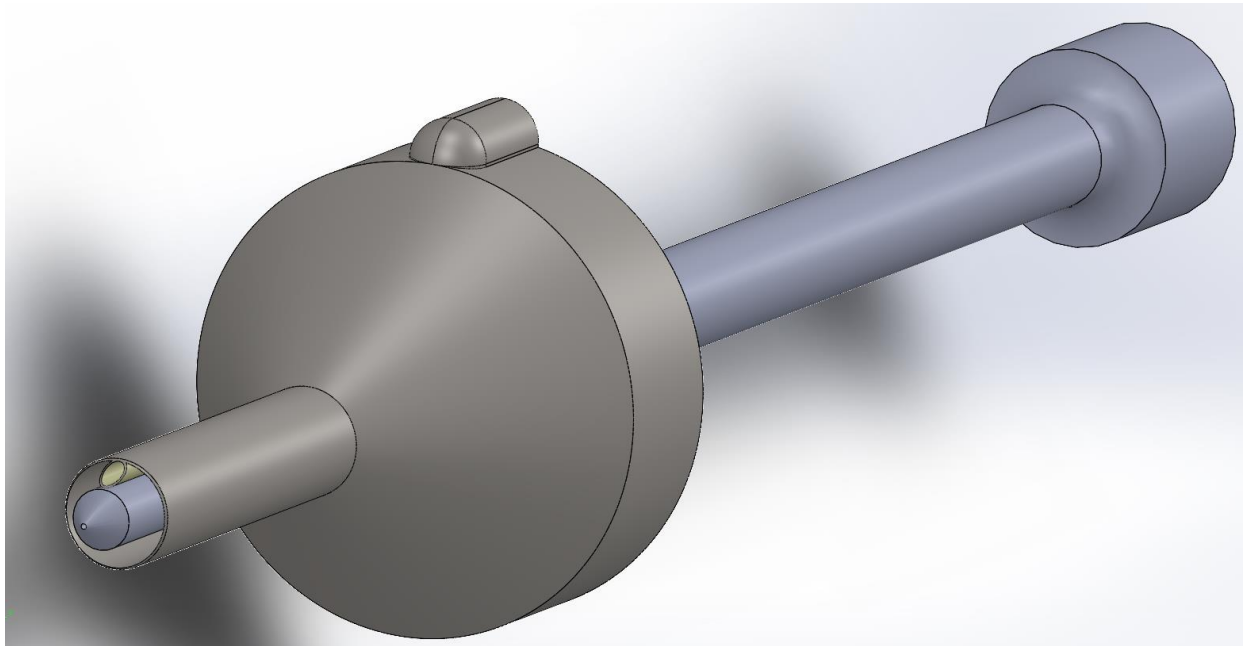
Модель з'єднання рупора з ковпачком
